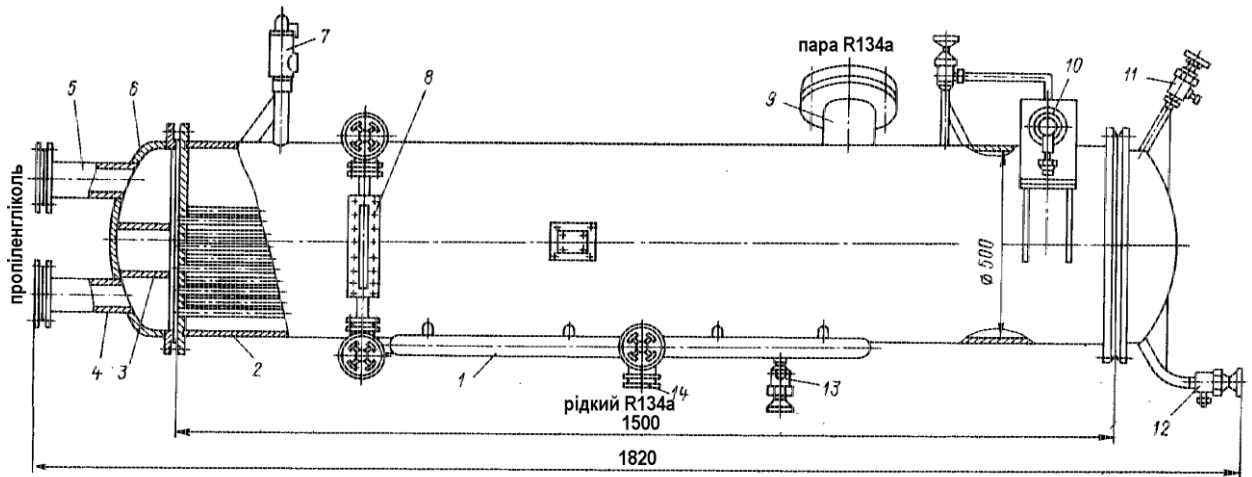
Зовнішній вигляд фреонового випарника типу ИТГ затопленого типу
